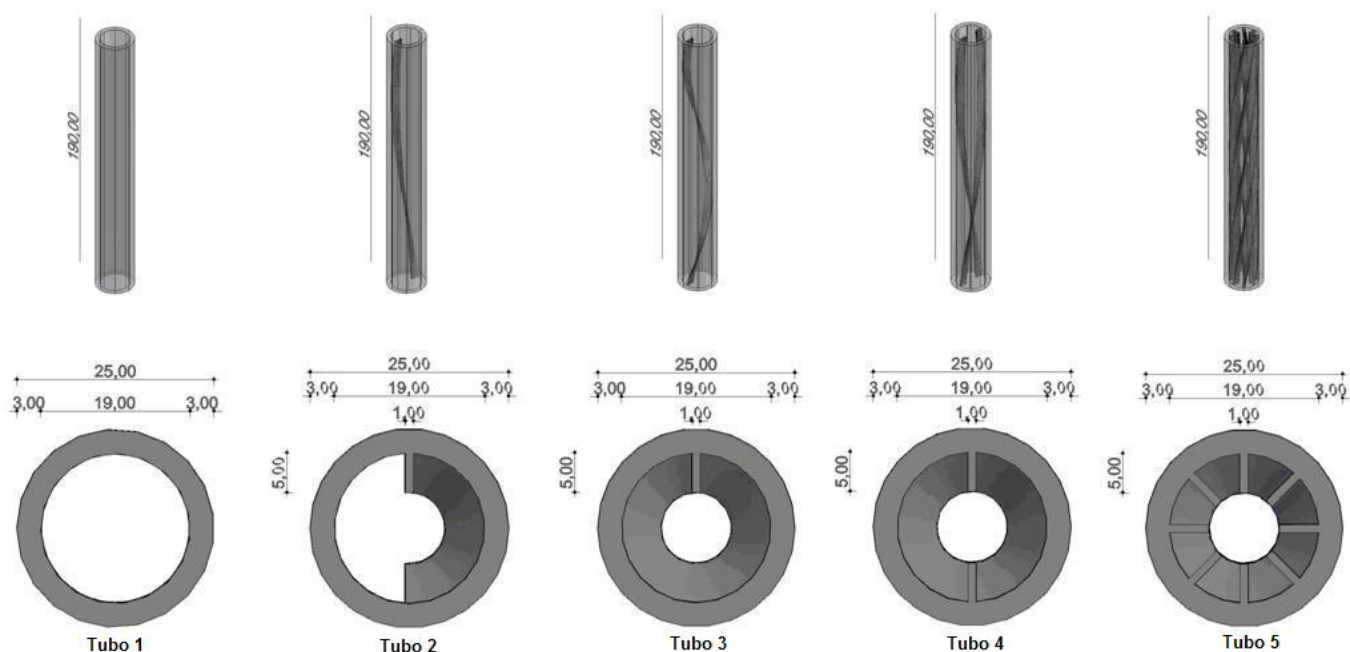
Vista isométrica e superior dos protótipos (dimensões em milímetros).
